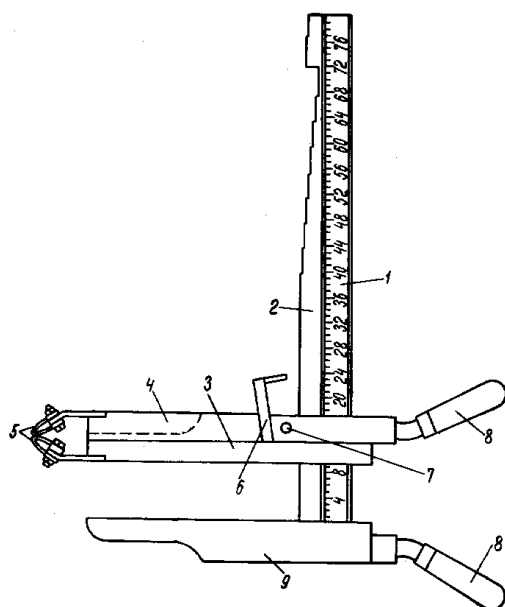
Вилка-разметчик конструкции КирНИИЛП:
